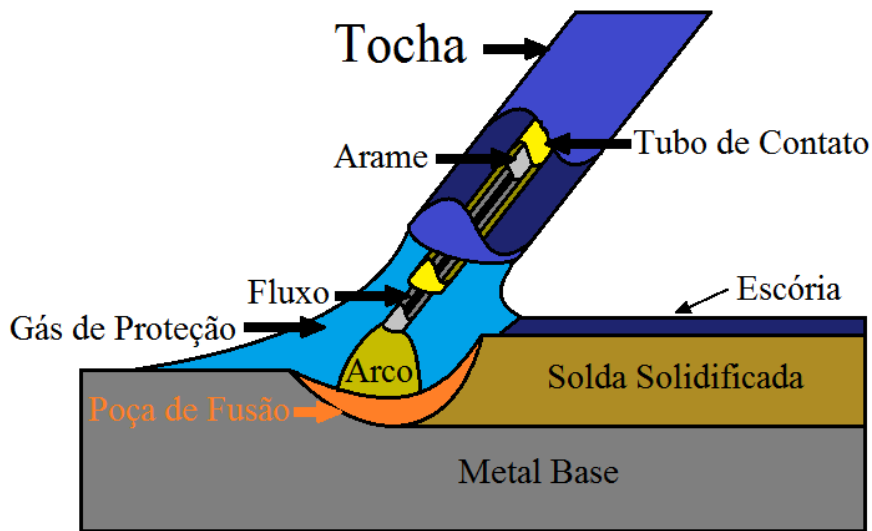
Diagrama: Flux-Cored Arc Welding (FCAW)
